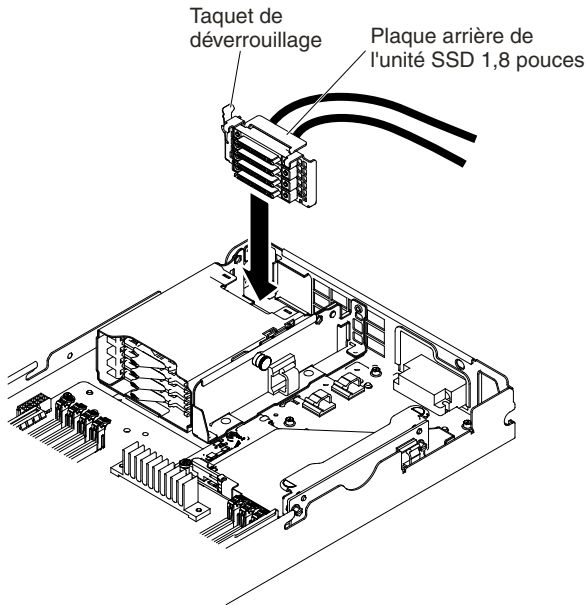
Installation de la plaque arrière pour les unités 1,8 pouces
